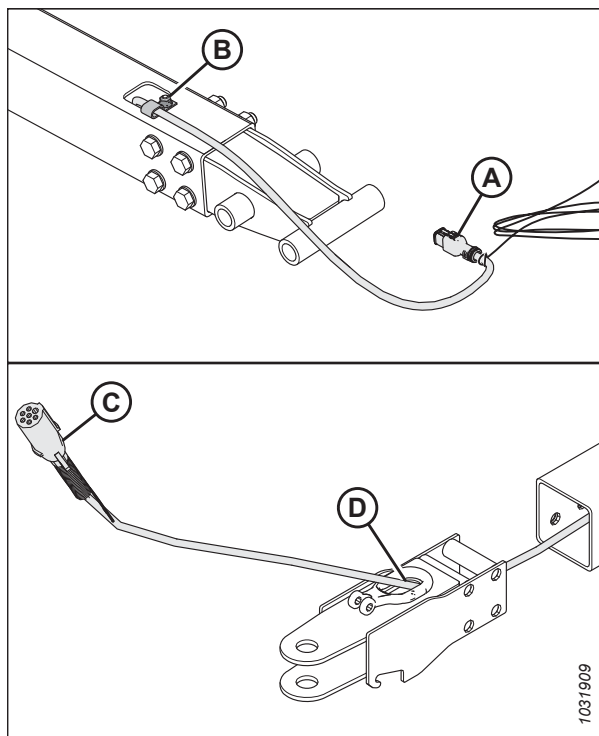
Extracción del adaptador de remolque de la horquilla
